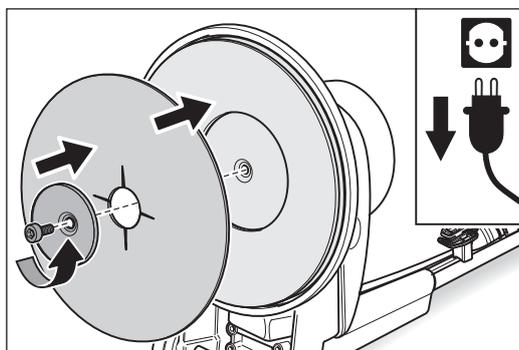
Auflegen der neuen Schleifscheibe und festschrauben. Die Schraube dabei gegen den Uhrzeigersinn drehen (Linksgewinde)!
